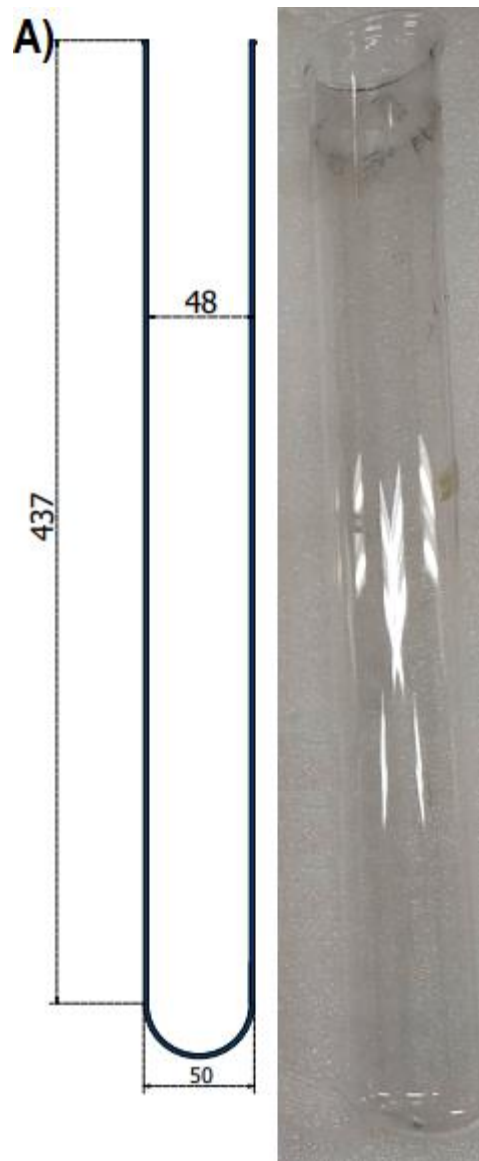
Cubierta de cuarzo. a) Plano vista lateral b) Foto lateral. Las dimensiones están en milímetros.
